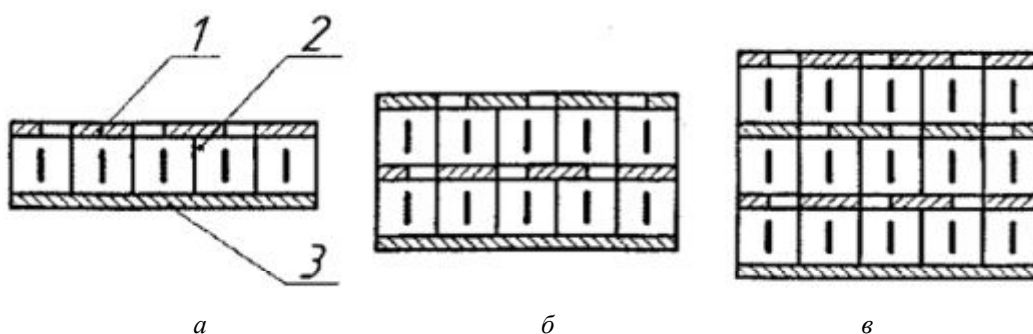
Основные типы и элементы конструкций с сотовым наполнителем:
